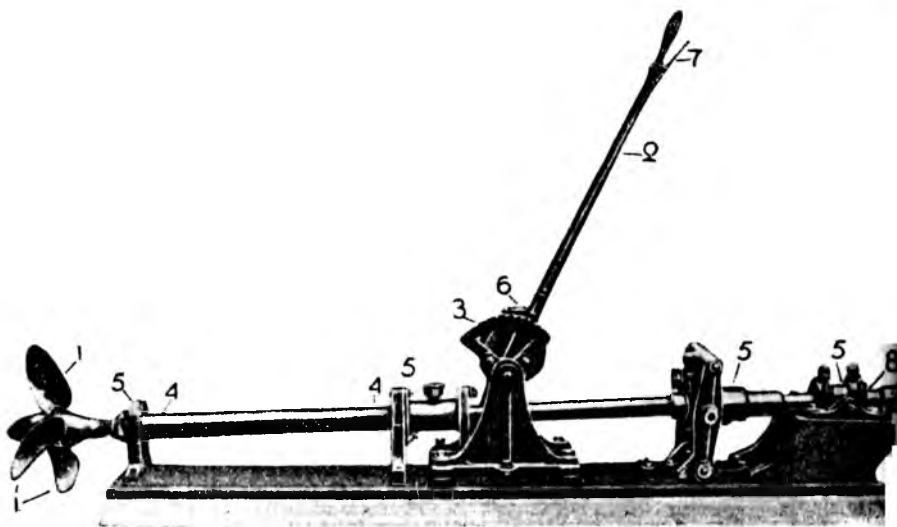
а. Винт с поворотными лопастями 1, с валом 8, и с подшипниками 5—5, направляющими и упорными.—4 и до 4, уширенная часть длины вала, для пропуска внутри тяг, поворачивающих лопасти.—2, рычаг для перестановки лопастей, устанавливаемый по зарубкам 3 сектора, посредством собачки 6 и вспомогательной ручки 7.
